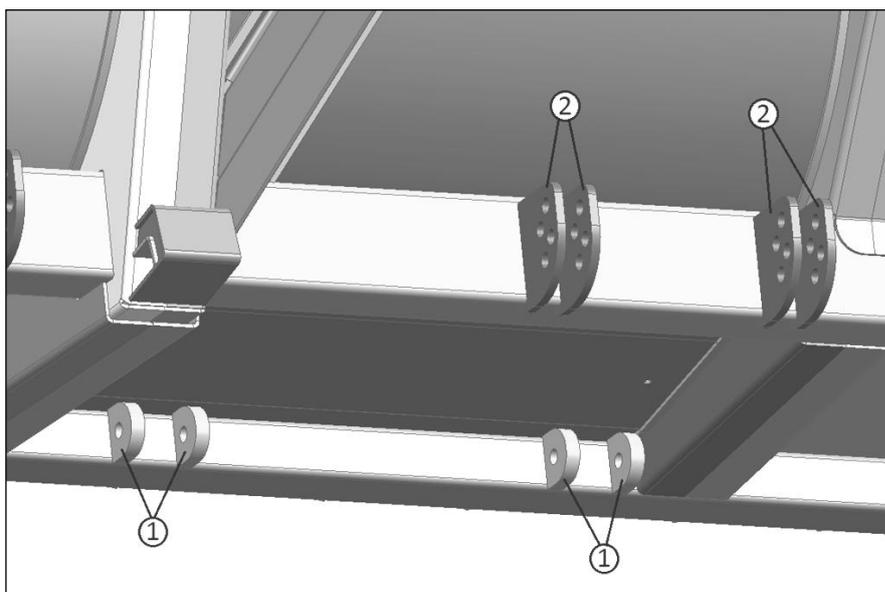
Дополнительный регулируемый опорный башмак
